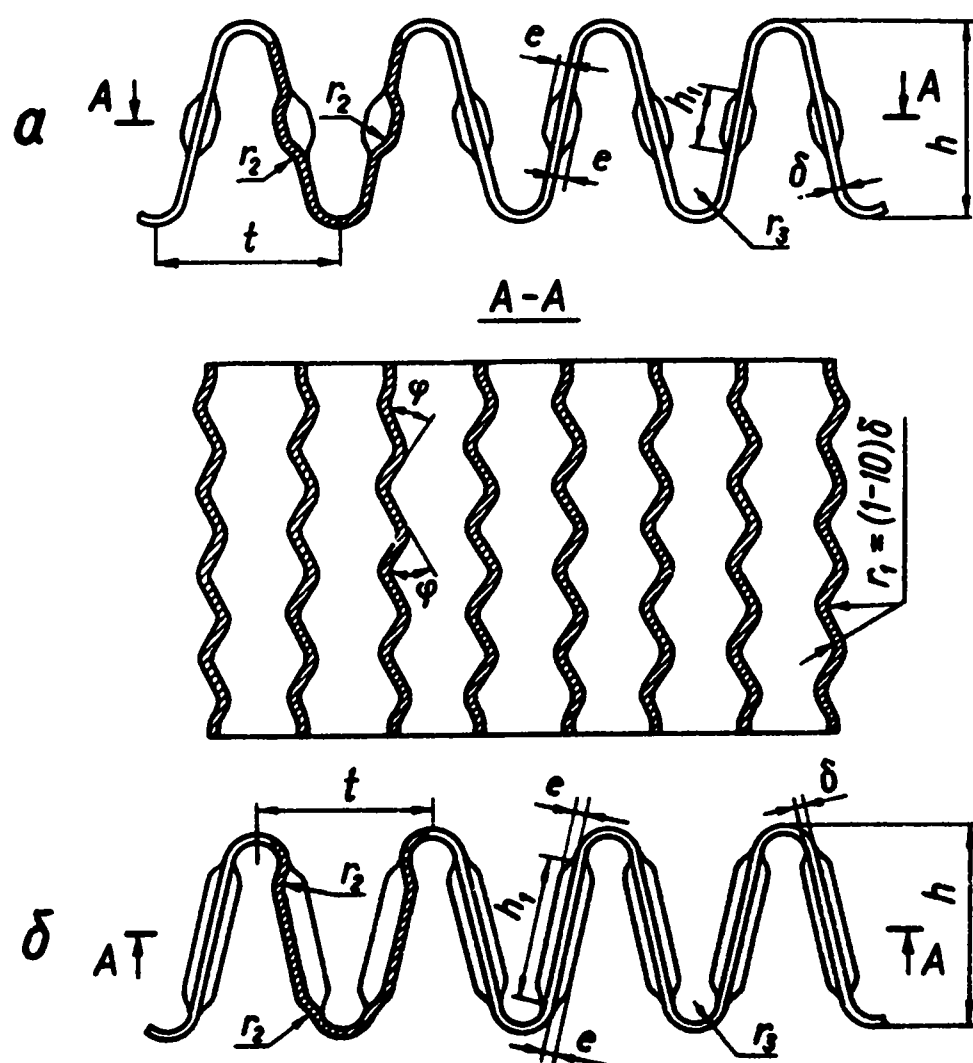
Треугольные каналы поверхностей с непрерывно сопряженными двухмерными выступами и канавками. а, б — различные варианты конструктивного выполнения
